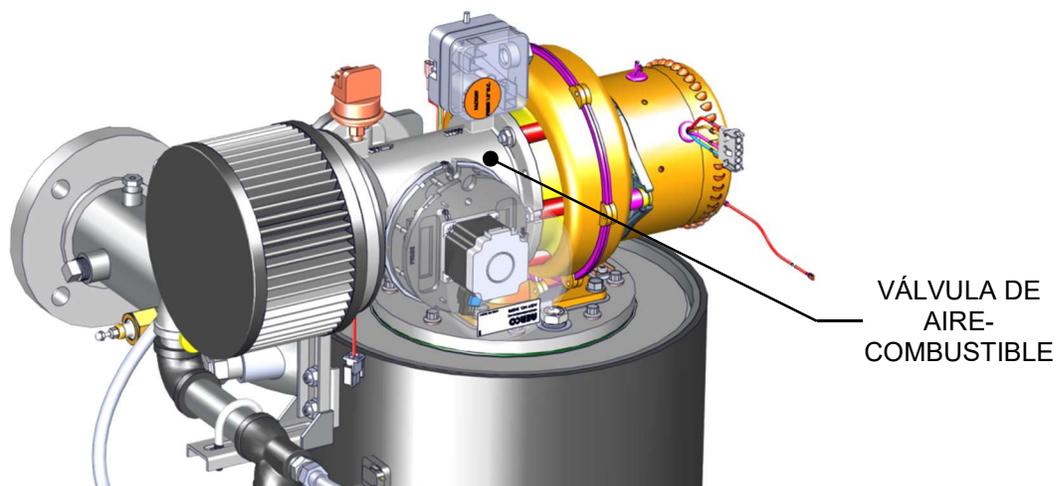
Estructura de caldera descubierta – Vista parcial
